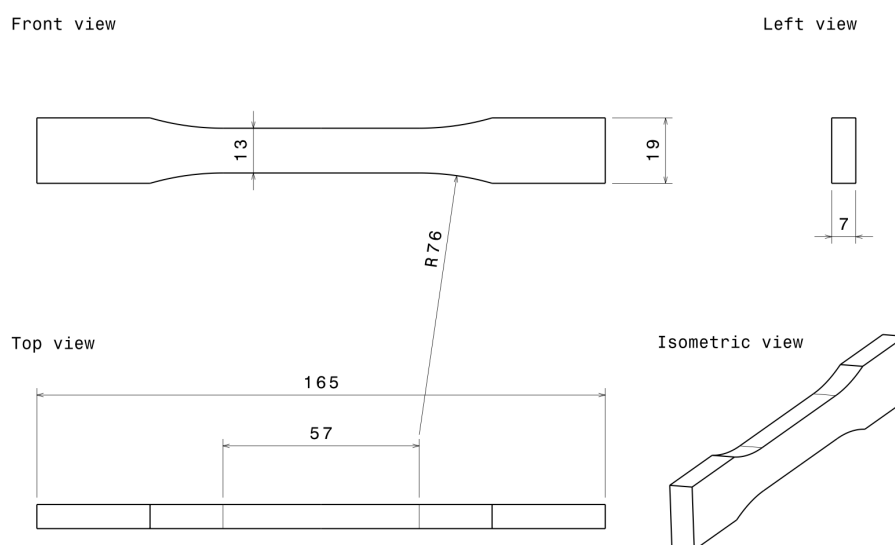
Geometría del espécimen a tracción (medidas en mm).
